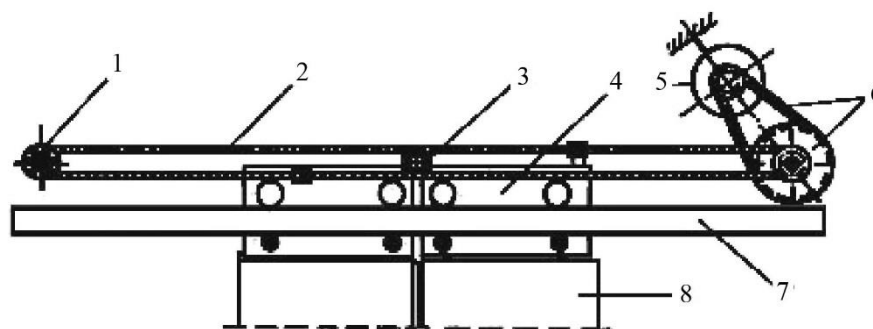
Автоматические двери с зубчатой ременной передачей:
